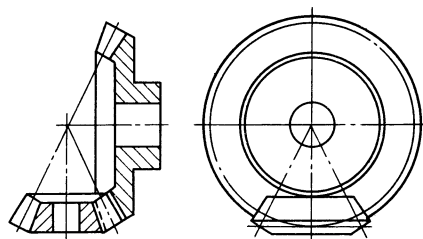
Условное изображение зацепления коническими зубчатыми колесами
